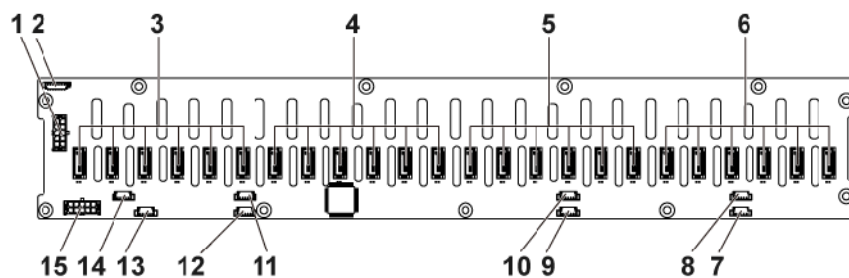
Vue arrière du fond de panier de disque dur de 2,5 pouces
